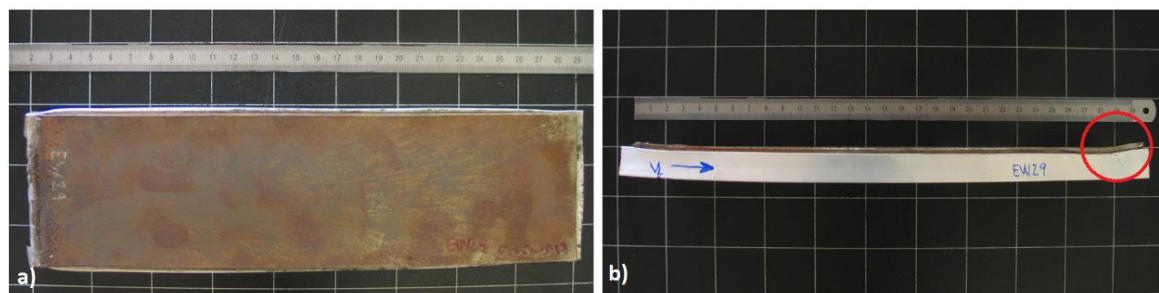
Análise macroscópica da soldadura EW29: a) Vista de topo; b) Vista de lado.
